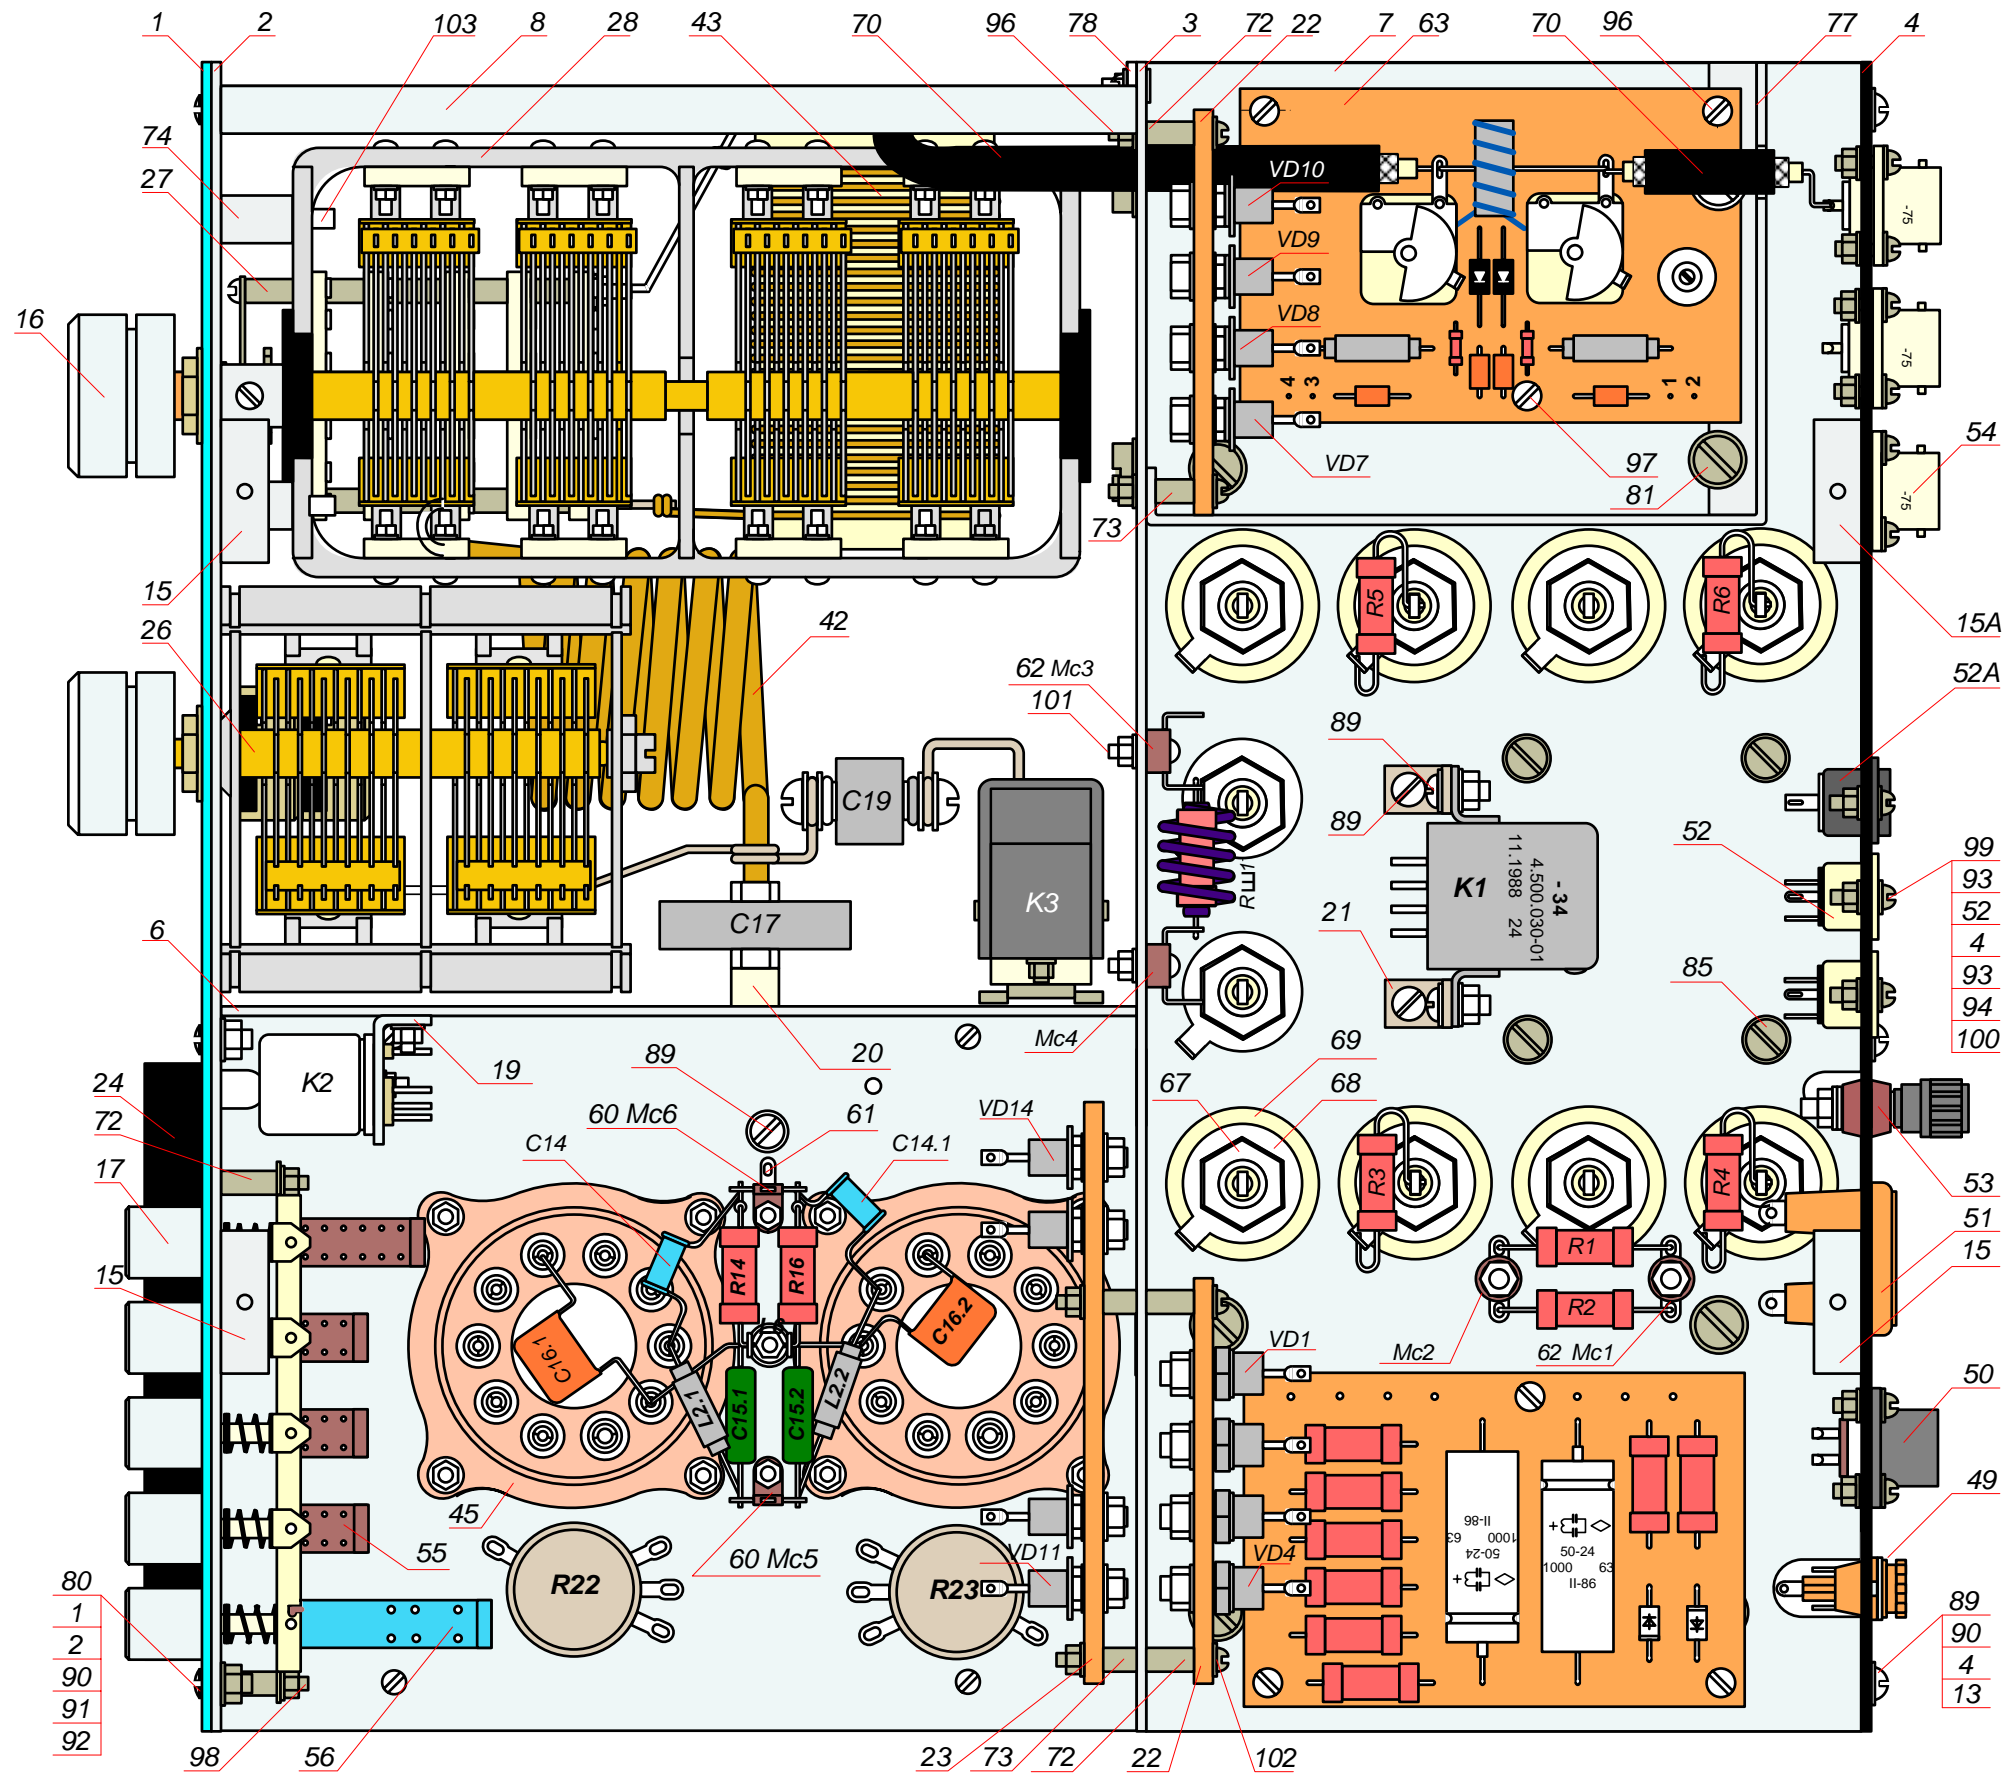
В. Сборочный чертёж усилителя DVA-300В. Вид сверху со снятыми верхней и нижней крышками.
